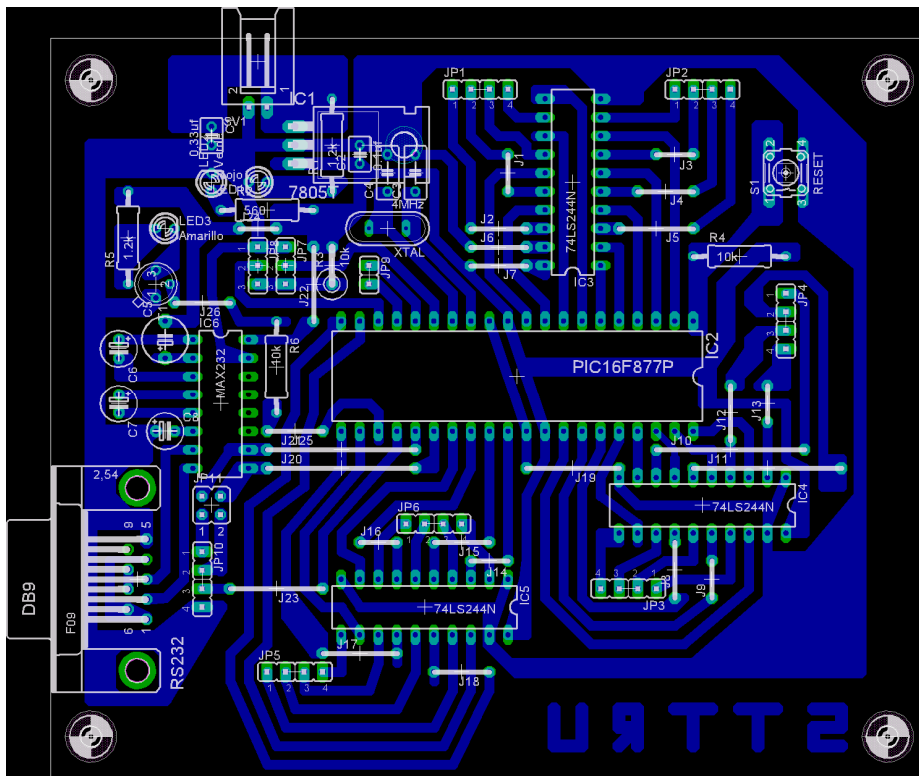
Tarjeta Control STTRU Vista de Componentes e Impreso
